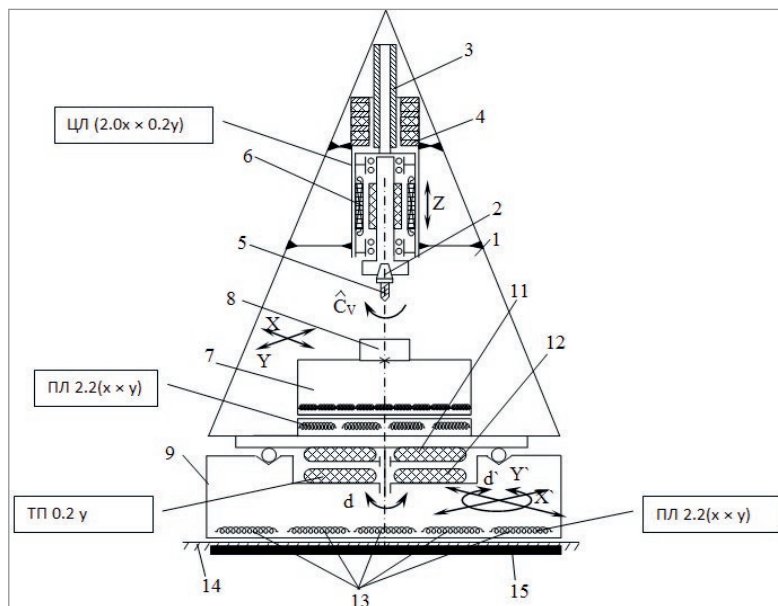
Багатокоординатний мобільний свердильно-фрезерний верстат майбутнього без механічних передач з генетичними формулами вузлів (механізмів)
